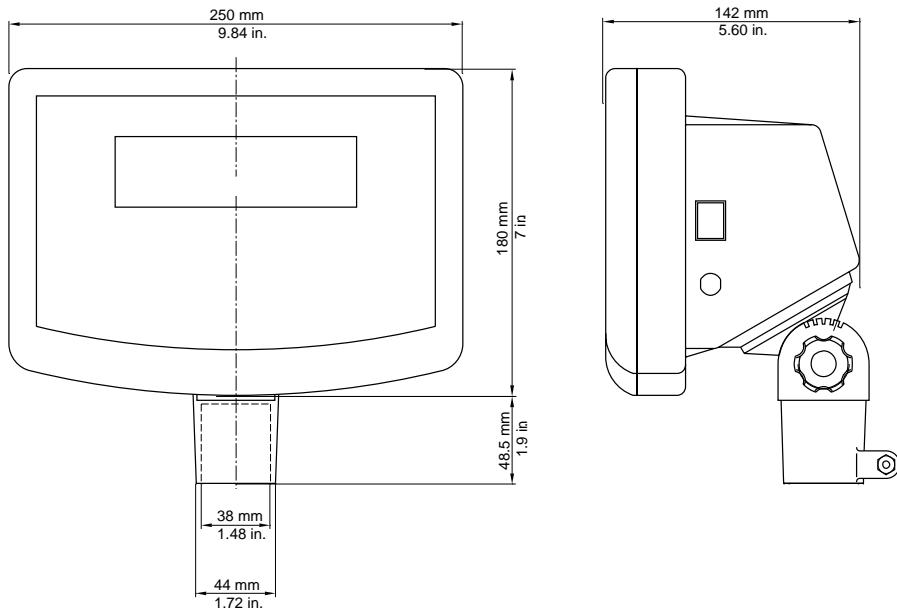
Dimensions hors-tout de l'indicateur T21P
